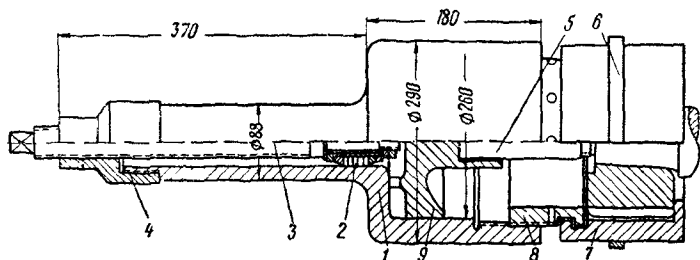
Гидравлическое приспособление для снятия шестерни с вала тягового двигателя:
